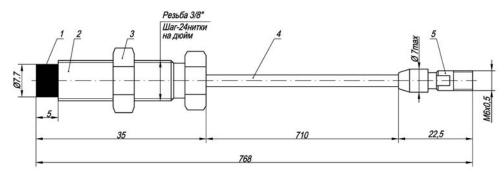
Преобразователь вихретоковый ИЦФР.408113.012 (код ПВ18): 1 – наконечник; 2 – корпус; 3 – гайка; 4 – кабель; 5 – розетка СР-50-106ФВ
